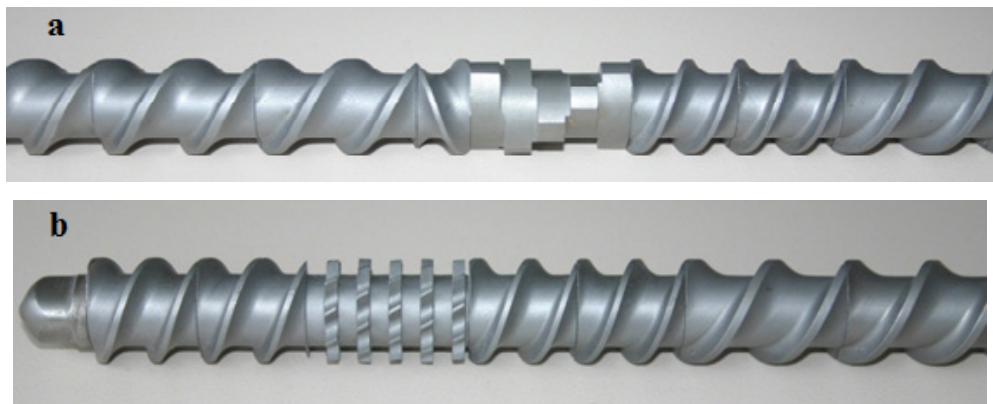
Elementos ensamblados de una extrusora de doble tornillo
